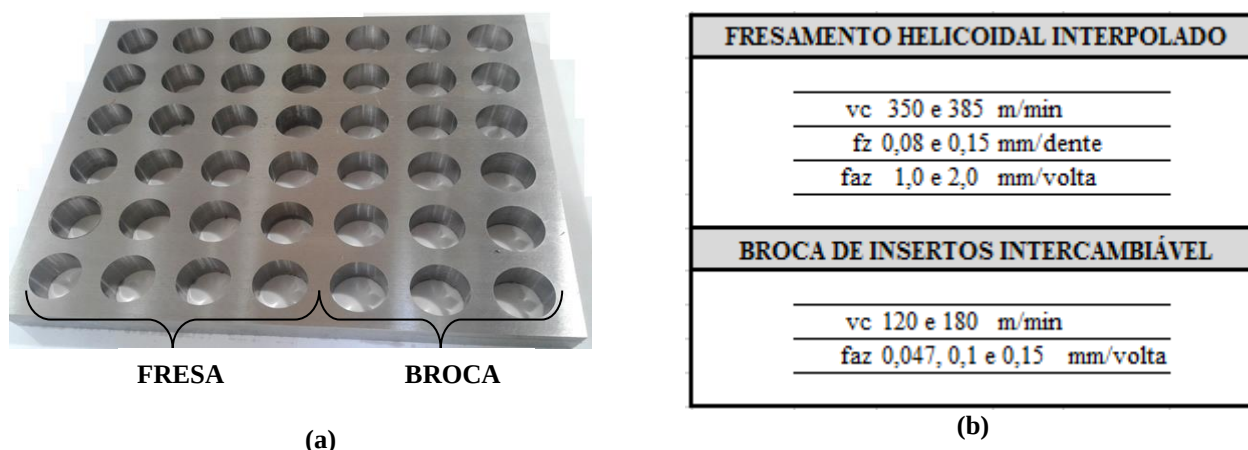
Condições de usinagem (a) Disposição dos furos com 8 condições para o fresamento e 6 condições para broca (b) Parâmetros de corte utilizados
